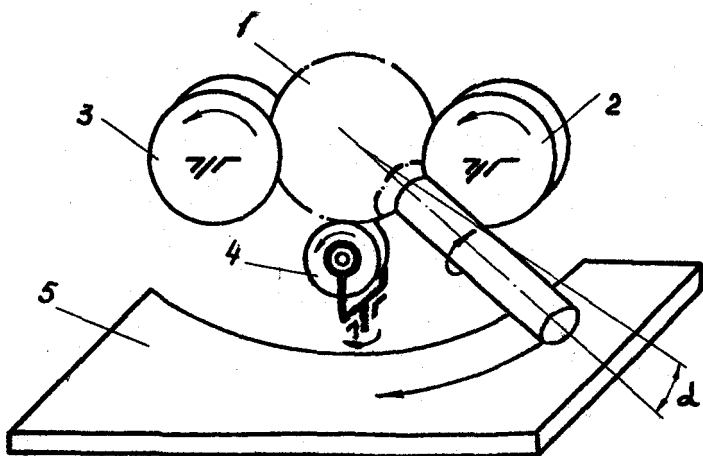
Схема устройства для бесцентрового накатывания сферических поверхностей
